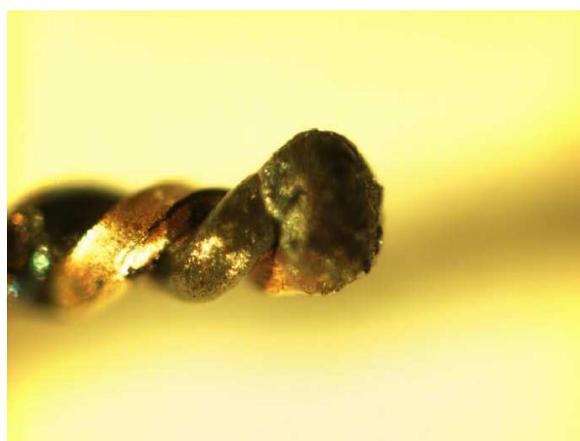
Amostra de solda do termopar tipo T de 32AWG.
